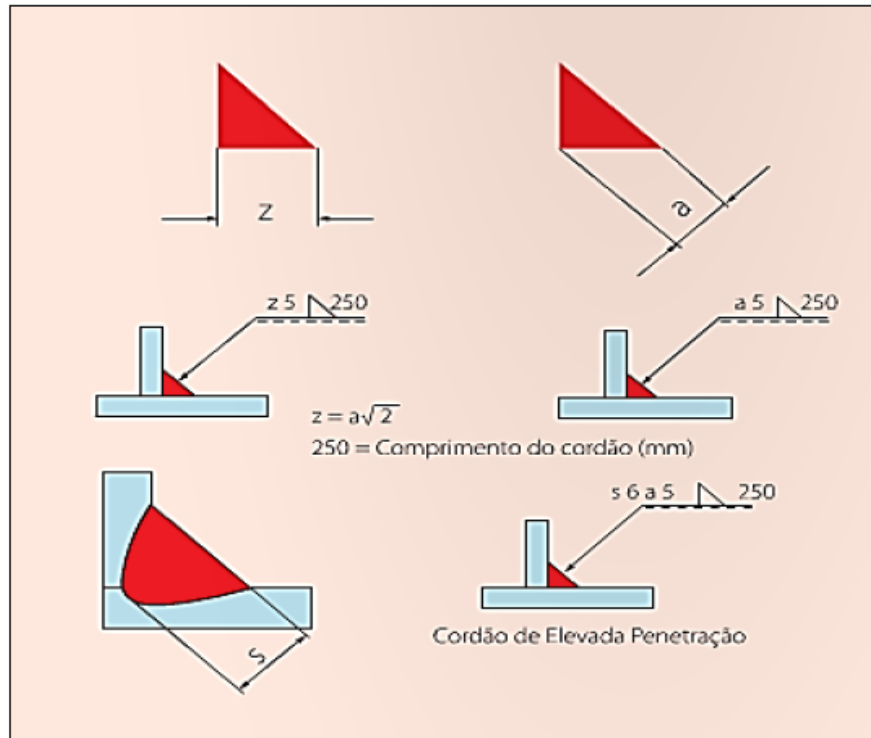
Representação das dimensões do cordão de soldadura segundo a norma ISO 2553 e AWS (z - Cateto da soldadura, a - altura da soldadura e s - soldadura + penetração) (Silva F. J., 2016)
